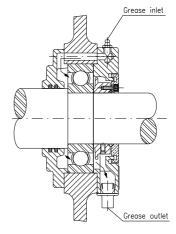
Поток смазки внутри корпуса подшипника.
